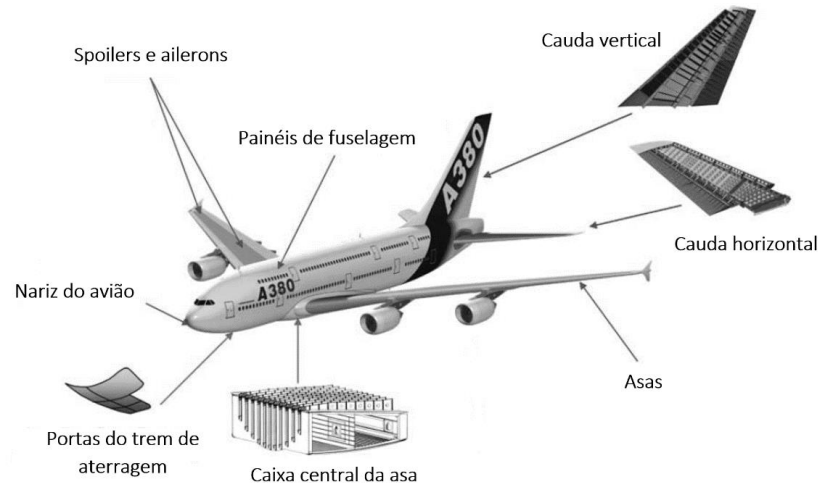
Aplicação de ligações adesivas na construção de um avião comercial [9]
